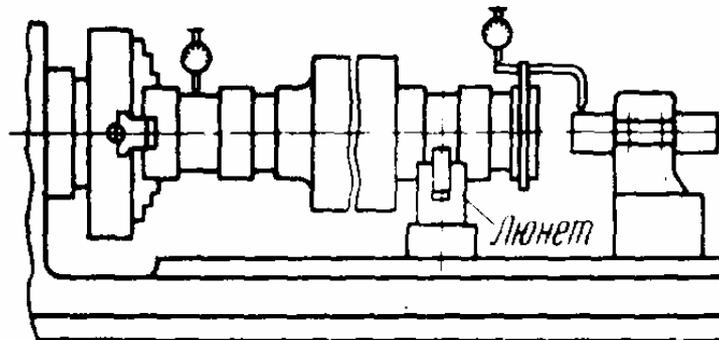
Схема установки заготовки в патроне и неподвижном люнете с выверкой
